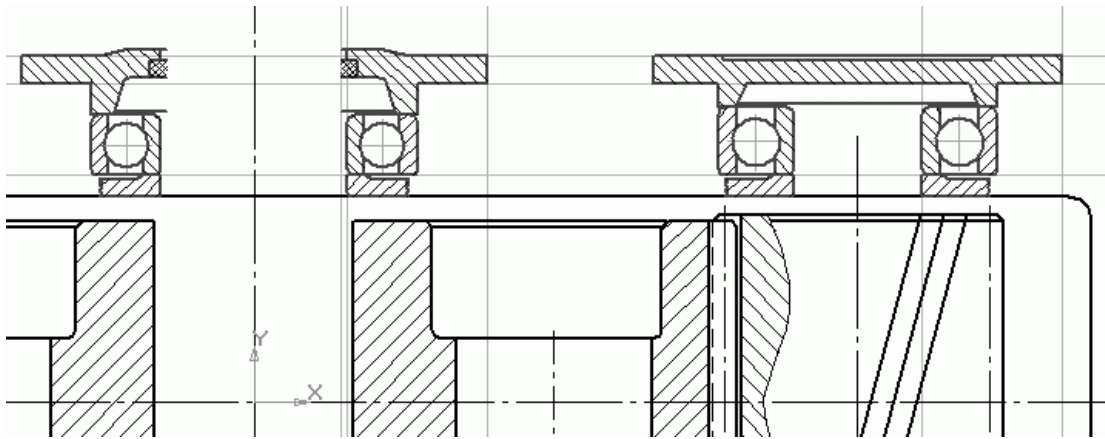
Подшипниковые узлы ведомого и ведущего валов
